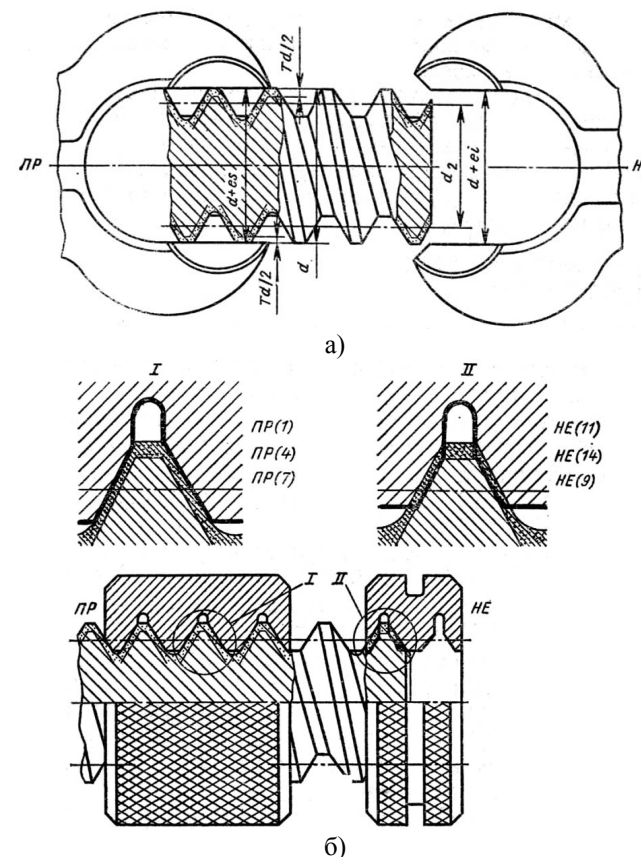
Гладкие калибры-скобы (а) и резьбовые калибры-кольца (б) для контроля наружной резьбы
